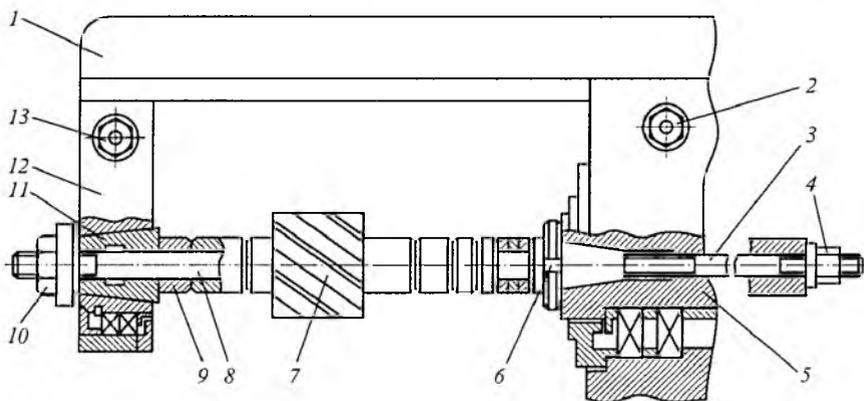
Оправка для установки цилиндрических и дисковых фрез:
